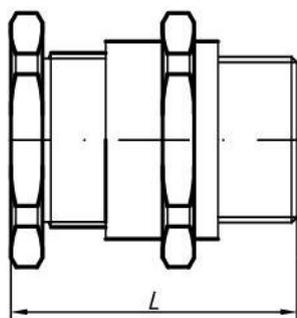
Кабельный ввод КНК для открытой прокладки кабеля,
